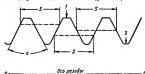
Профиль резьбы: 1 — вершина профиля; 2 — впадина профиля.
